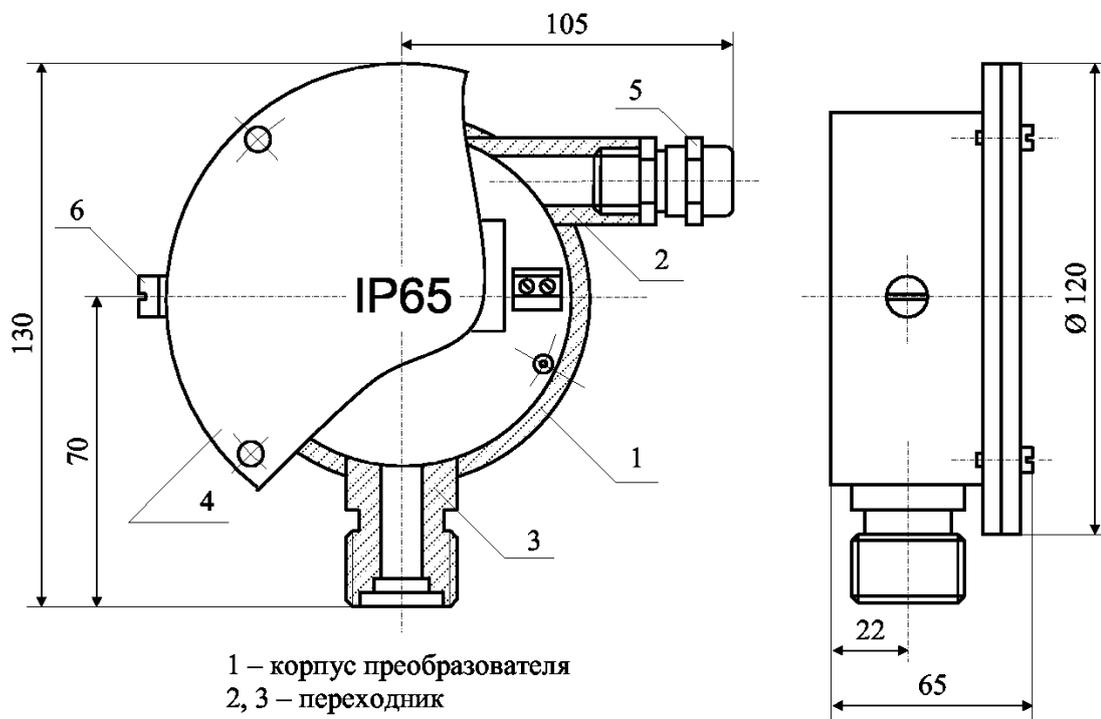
Корпус ПП из алюминиевого сплава
